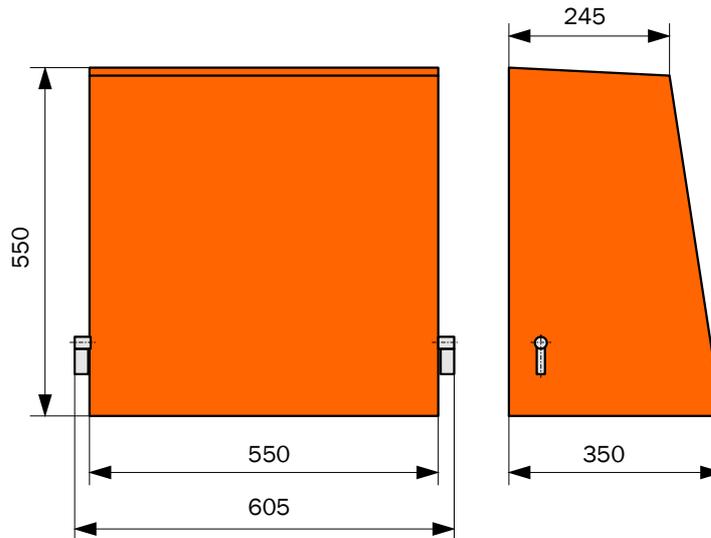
Погодозащитный кожух для узла подачи продувочного воздуха
